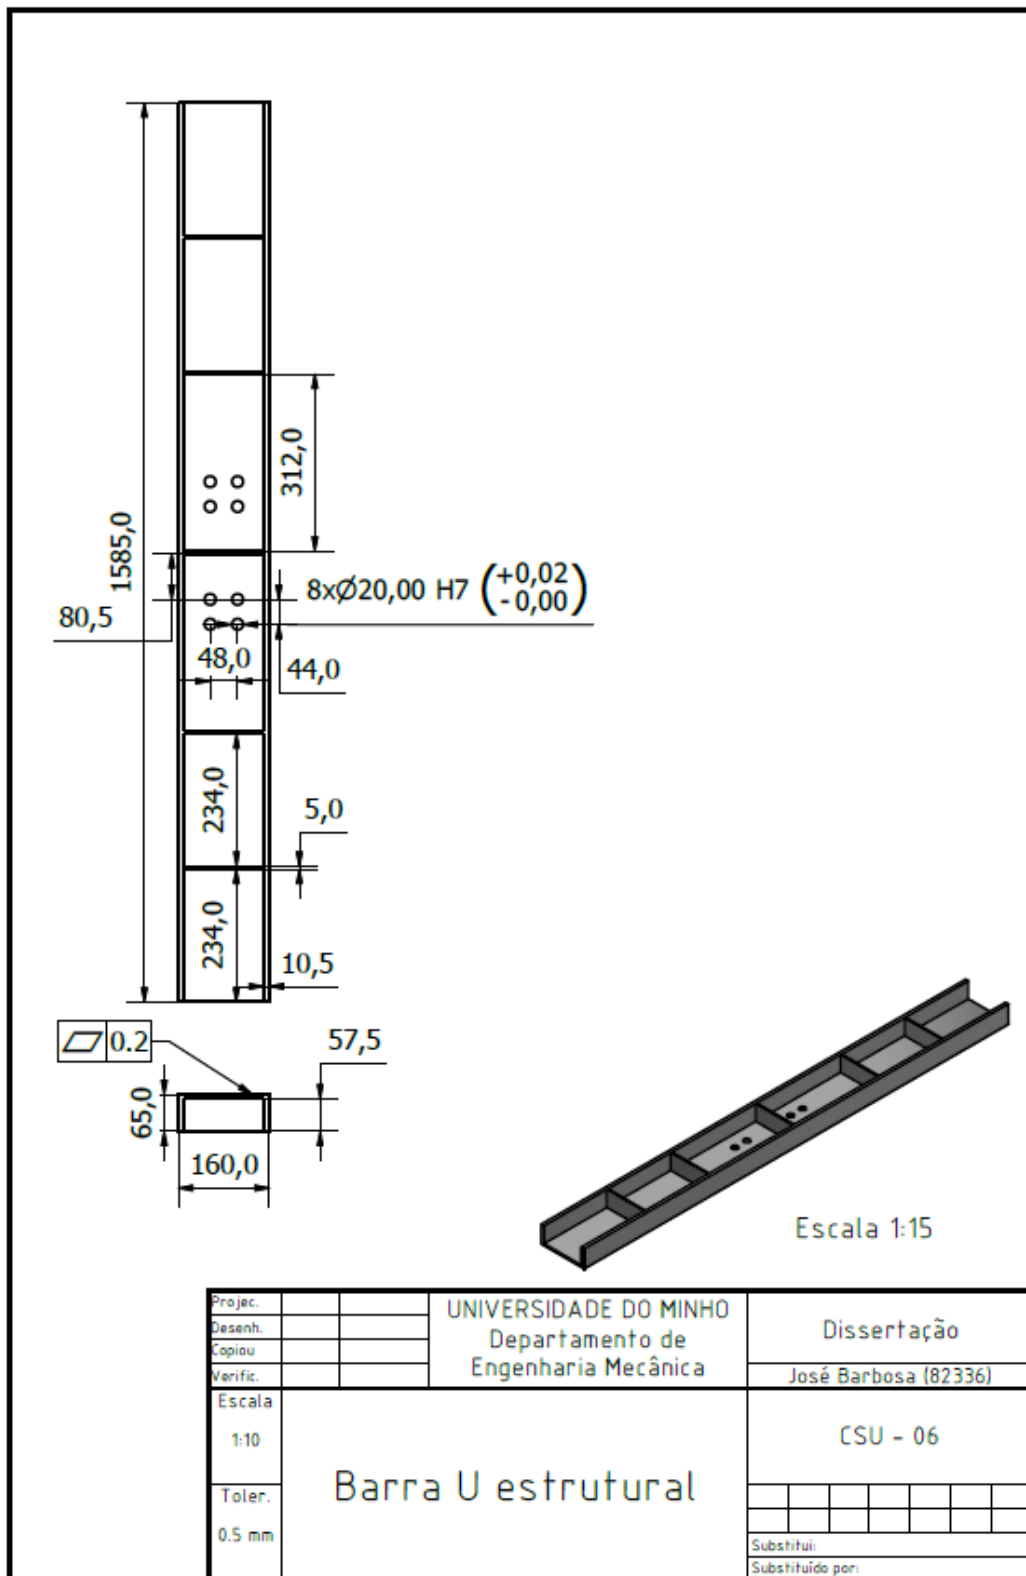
Figura anexo III-9 – Desenho técnico da barra U estrutural.
